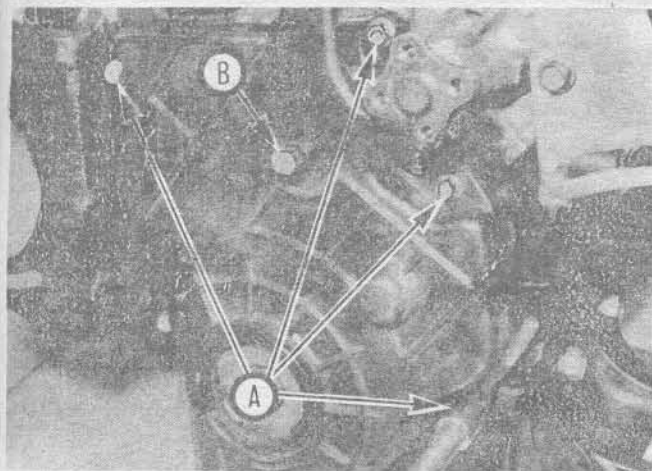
Для снятия нижней крышки привода ремня отверните болты А. Болт В используется только для регулировки натяжения ремня.
